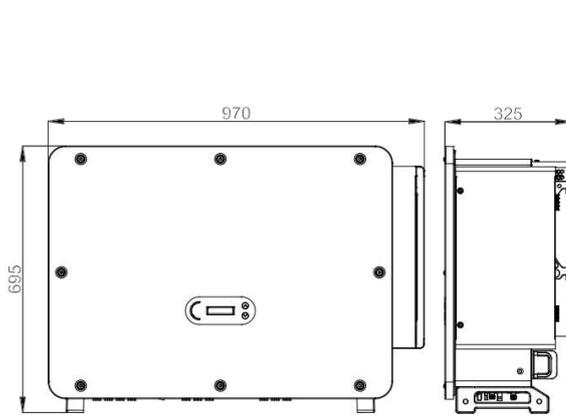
Vistas esquerda e frontal das dimensões do produto
